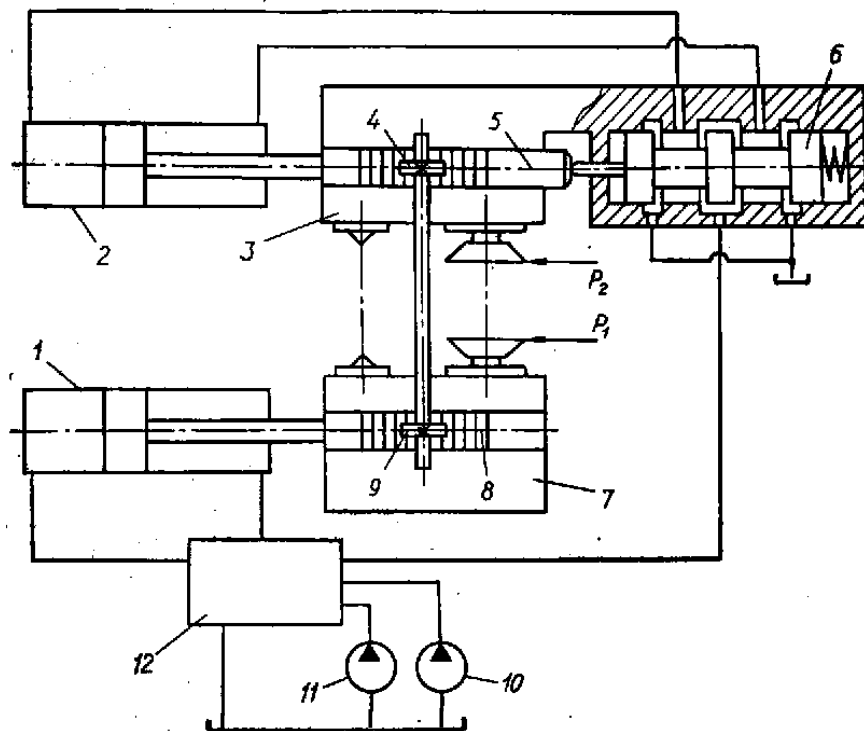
Схема синфазного привода робочих головок фрезерно-центрувальних напівавтоматів
